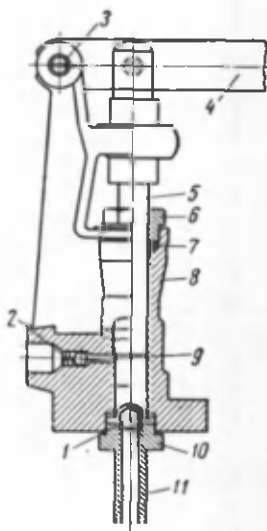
Конструкция малого цилиндра ручного гидравлического пресса:
